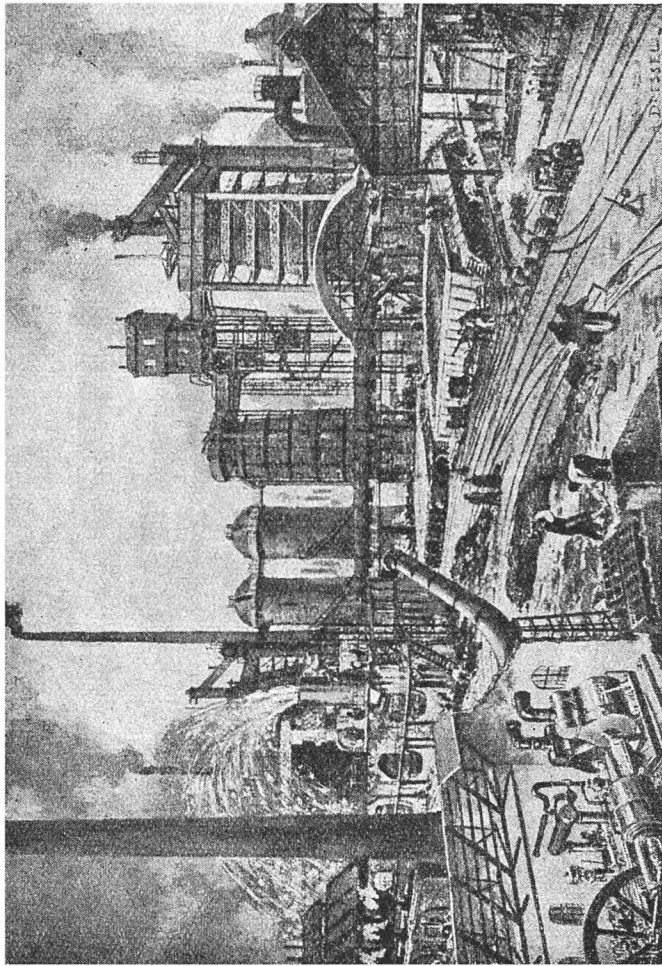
Чугуноплавильный завод за границей. Справа две домны с подъемной машиной, под ними площадки для отливки чугуна. В середине два каупера. Слева разрез воздуходувной машины, котлы для отливки стали.
